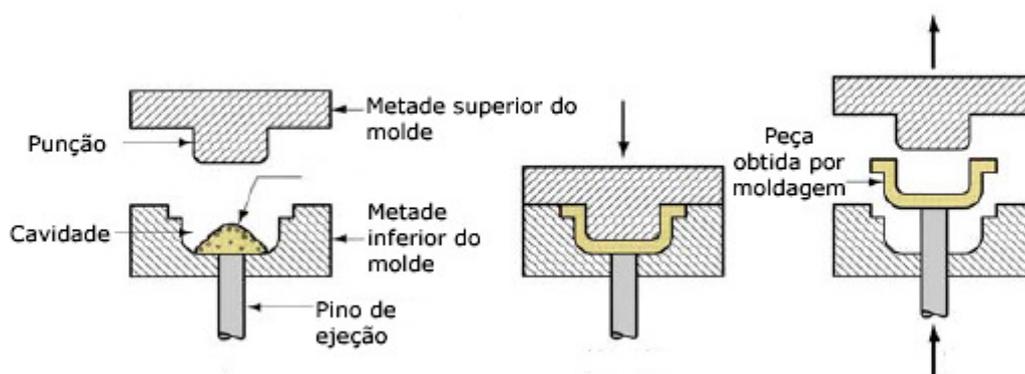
Moldagem por compressão. Fonte: Parente, 2006.
